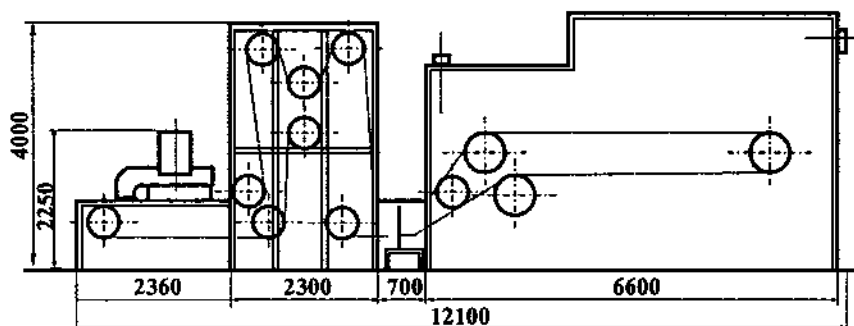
Расстойно-печной агрегат для формового хлеба П6-ХРМ
